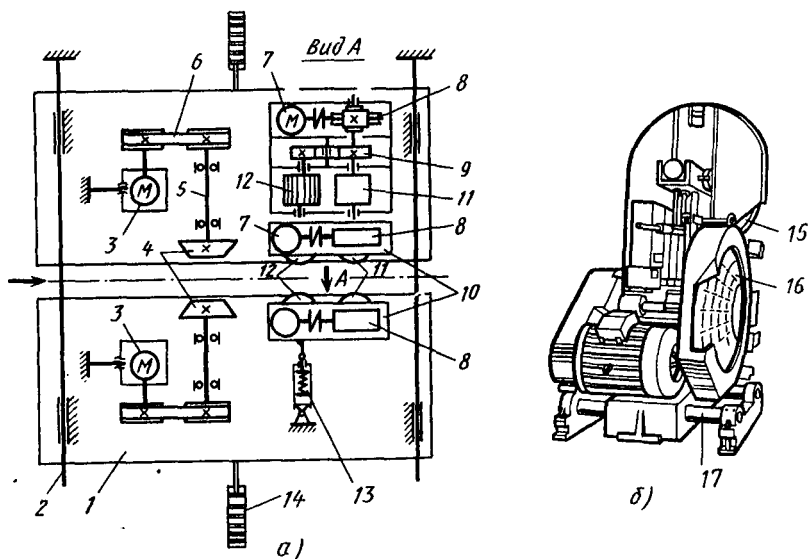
Сдвоенный фрезерно-брусующий станок ФБ-3:
